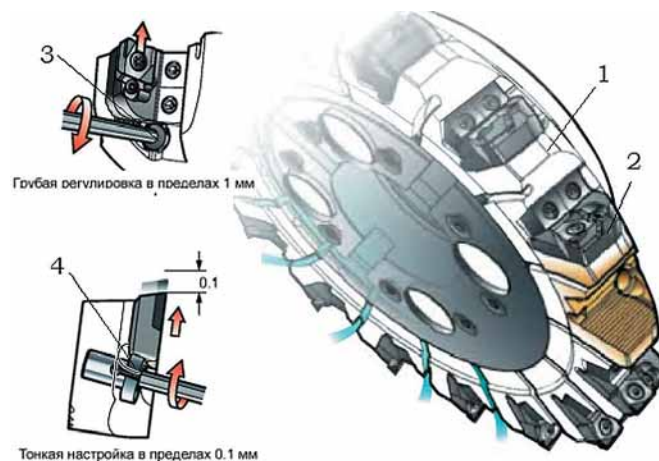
Торцевая фреза со сменными кассетами CoroMill Century
